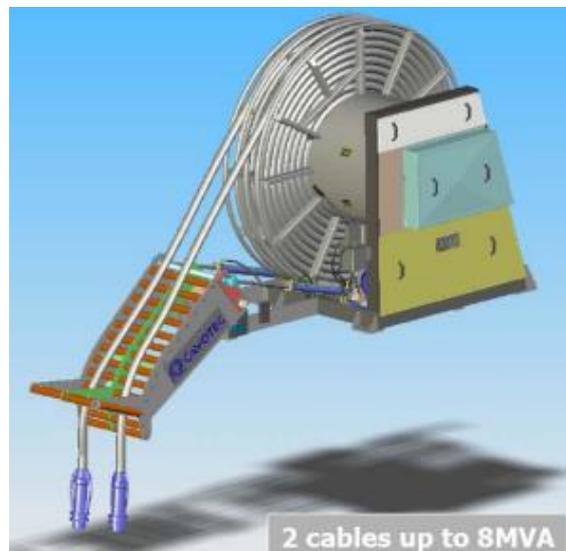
Carrete de 2 cables hasta 8 MVA.
